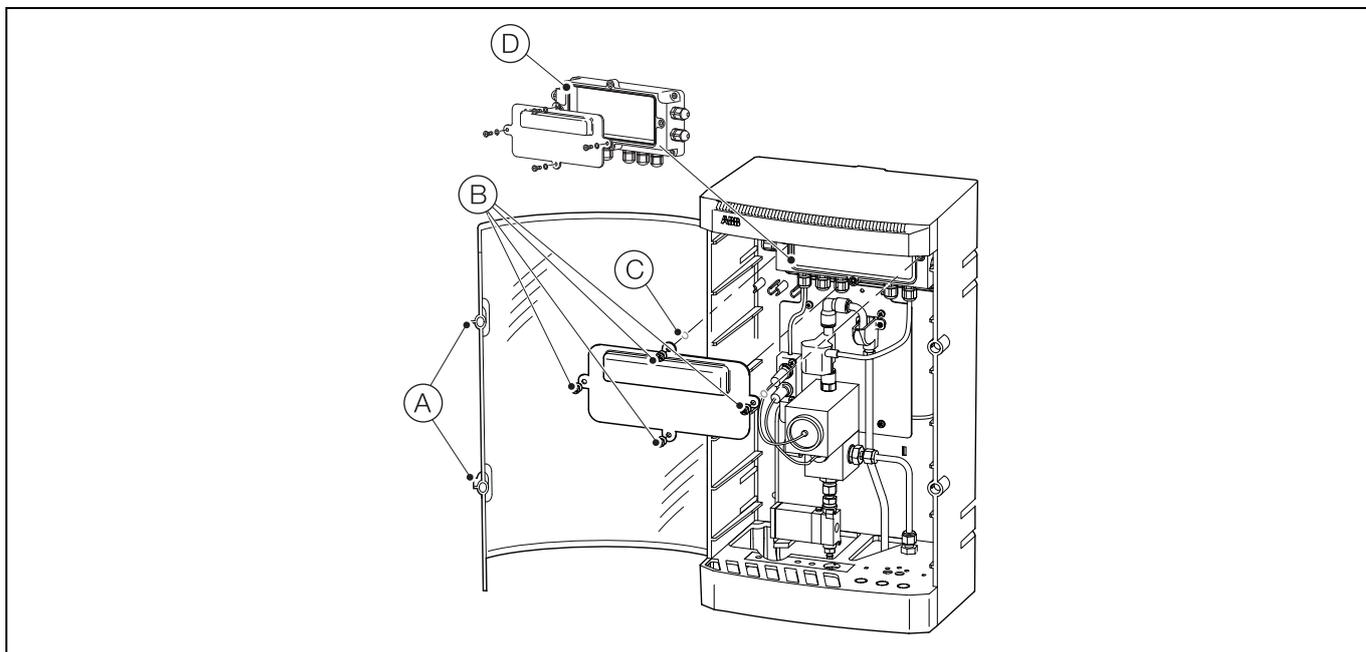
Acceso a la placa de circuito impreso de la sección de medición
